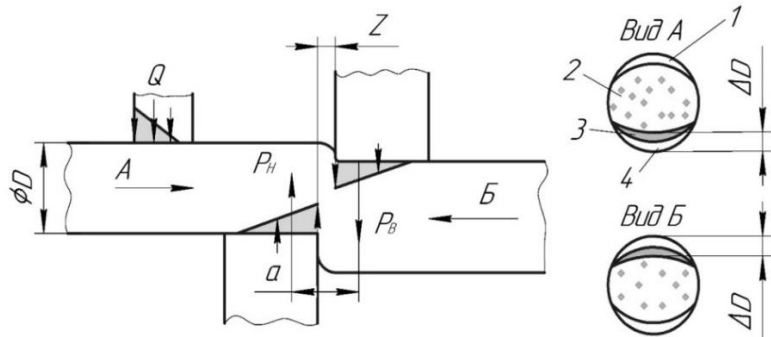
Схема действующих сил и напряжений при резке круглого прутка на ножницах
